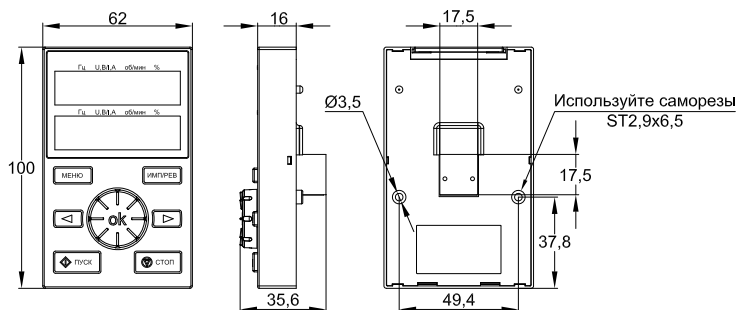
Габаритные размеры и размеры отверстий внешней цифровой двухстрочной панели управления (единица измерения – мм)
